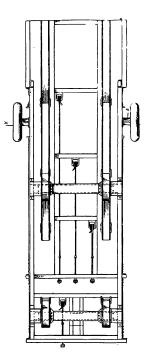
Деталь устройства опор для поддерживания задних колес автомобилей и полуприценке Мак-Гри.
